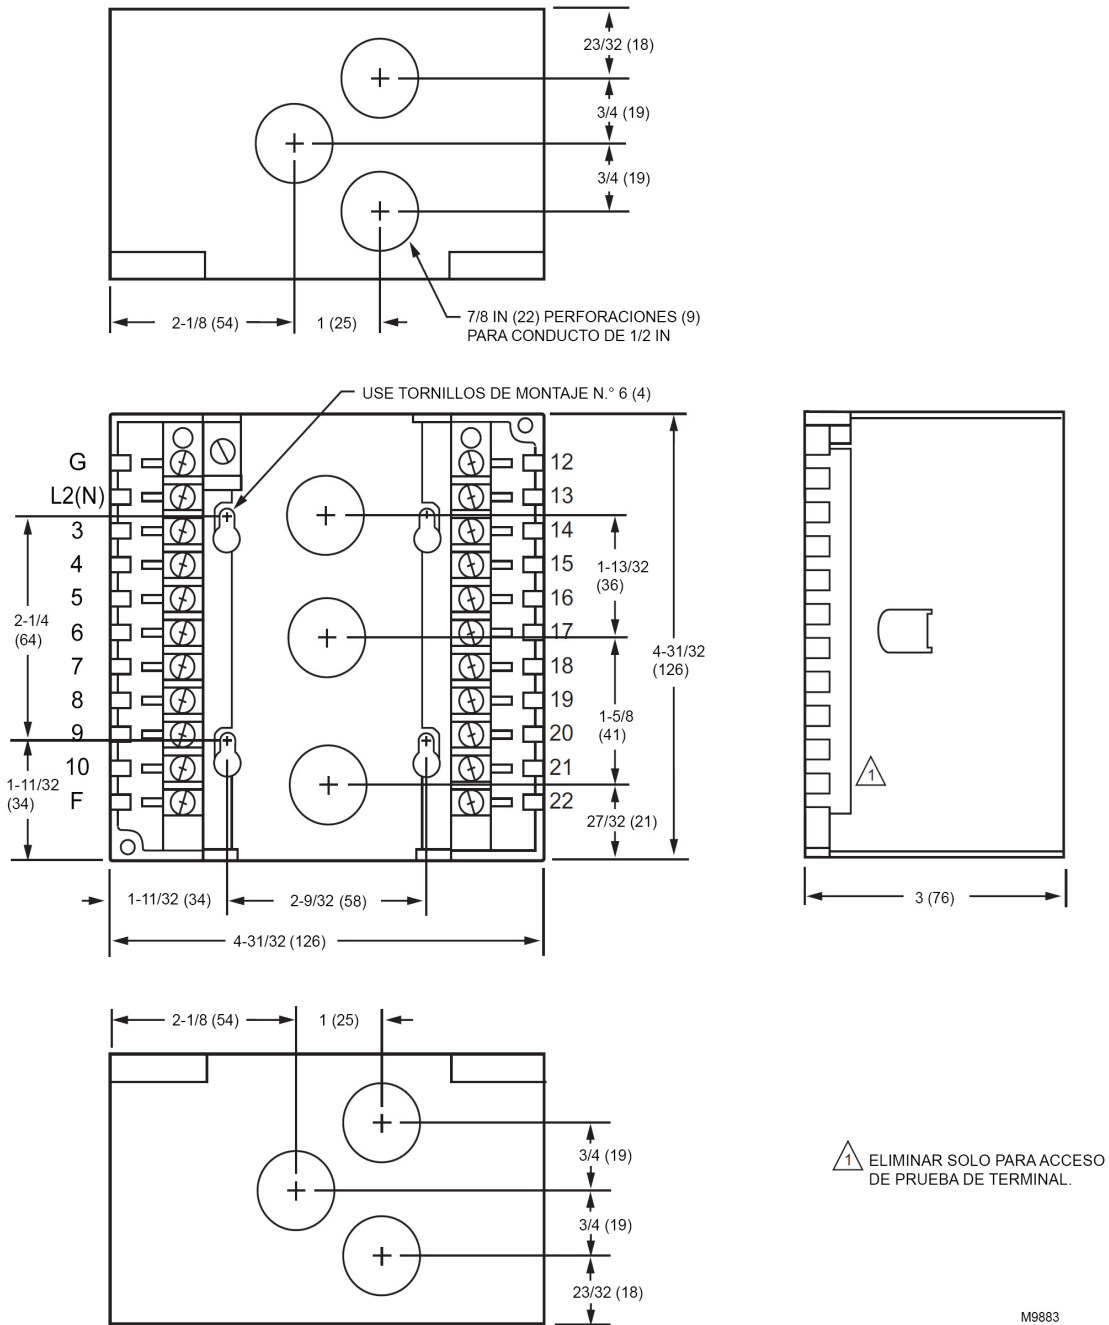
Vista superior y frontal de la subbase de cableado Q7800B1011 (4 caras) con dimensiones en pulgadas (mm).
